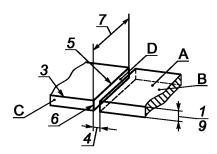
Подготовка под сварку стыкового соединения без скоса кромок
